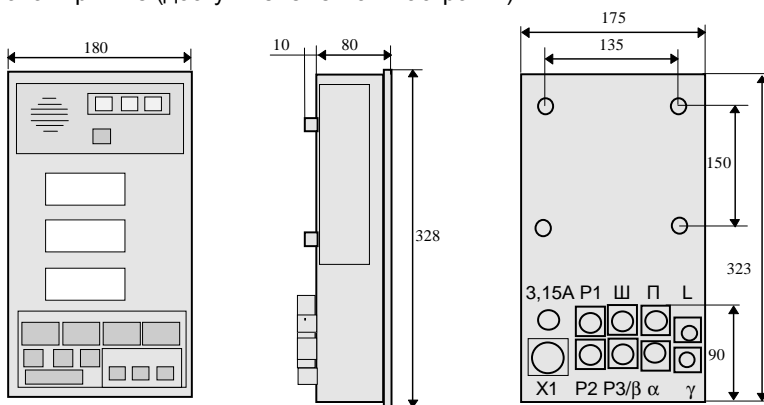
Габаритные и присоединительные размеры БОДа
